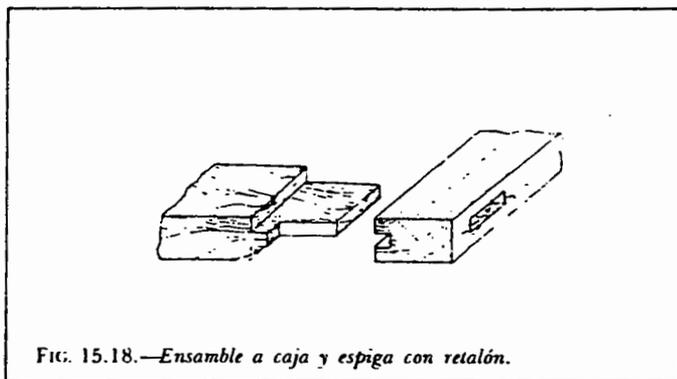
Ensamble a caja y espiga con retalón.
